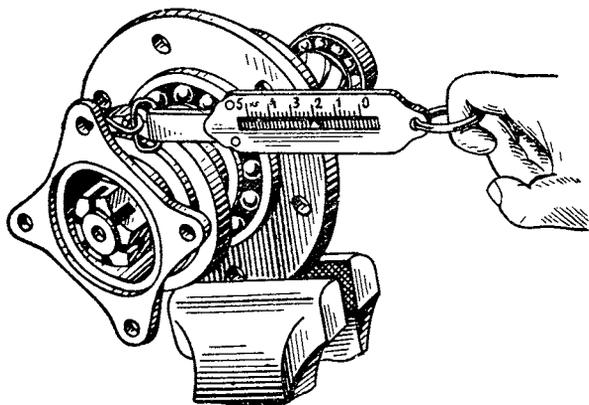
Проверка затяжки подшипников ведущей шестерни
